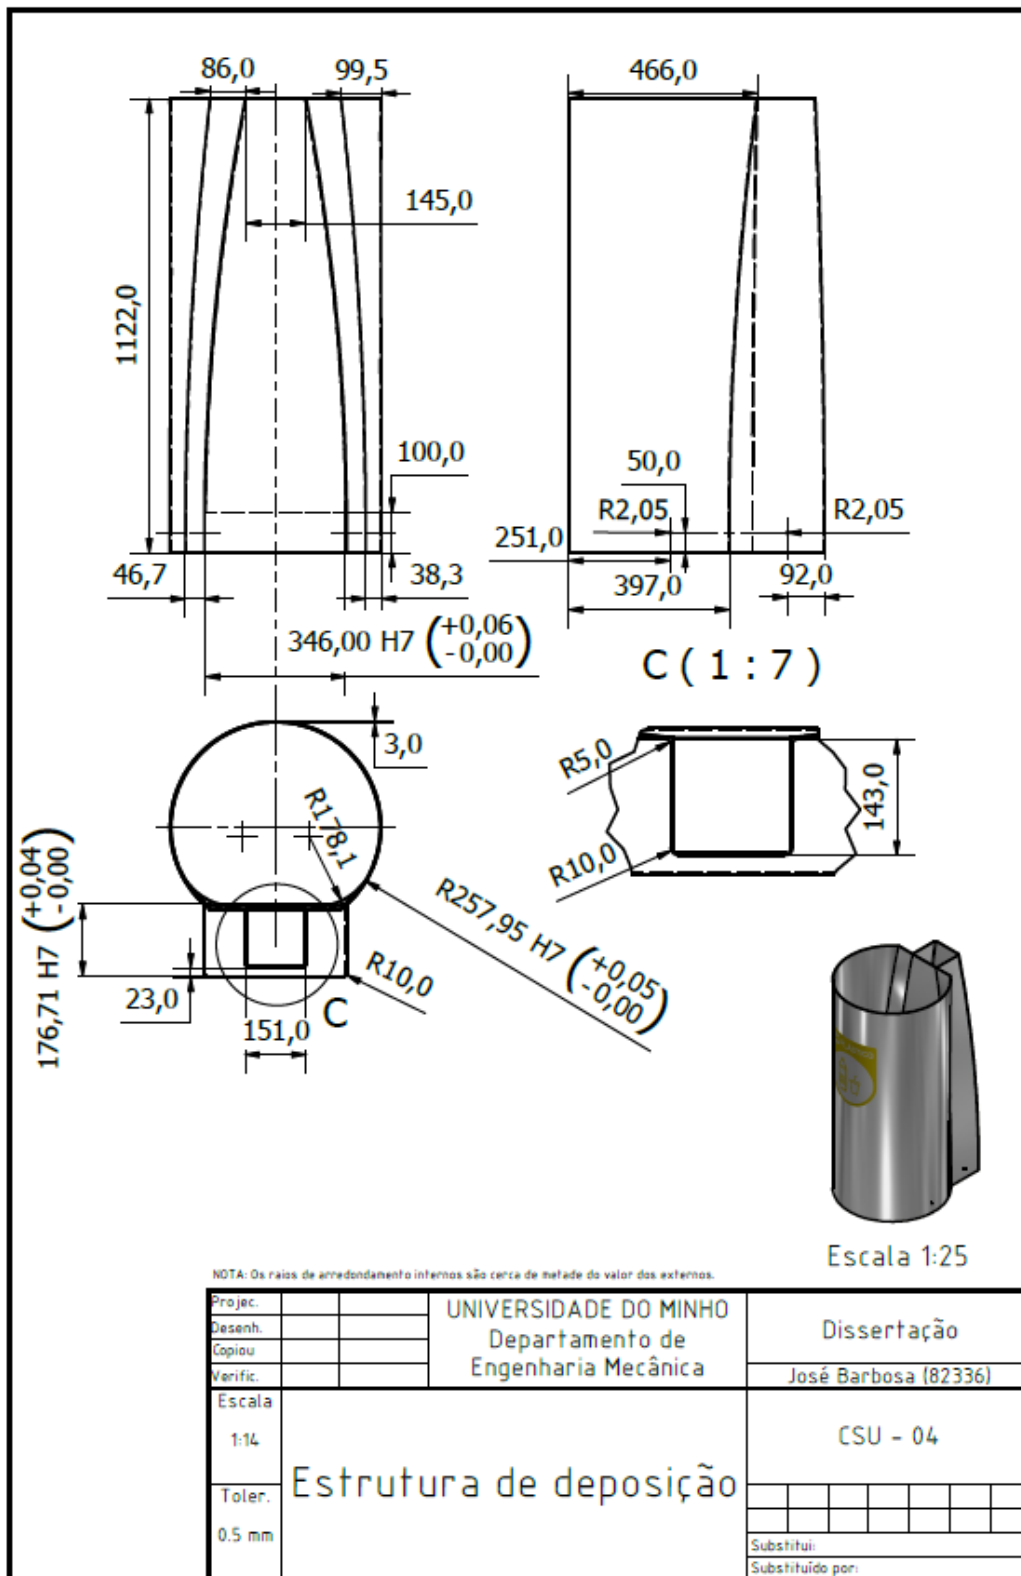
Figura Anexo III-7 – Desenho técnico da estrutura de deposição.
